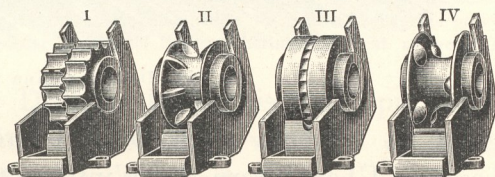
Wechselschubräder der Drillmaschine „Simplex“ von Fr. Dehne (I für Getreide, II für Rüben, Bohnen, Erbsen, III für Raps, IV für große Bohnen).
